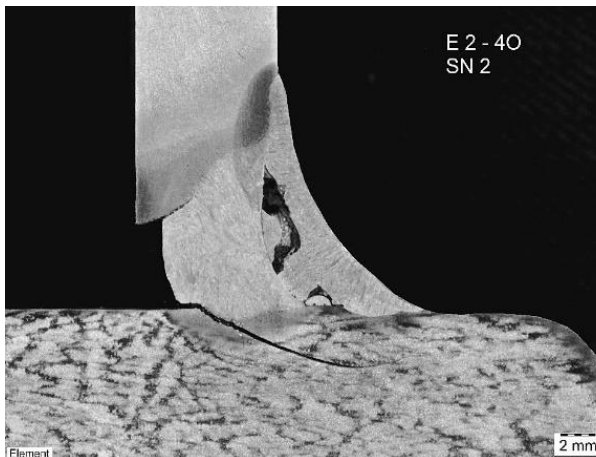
Schweißimperfektionen HY-Naht [21]
